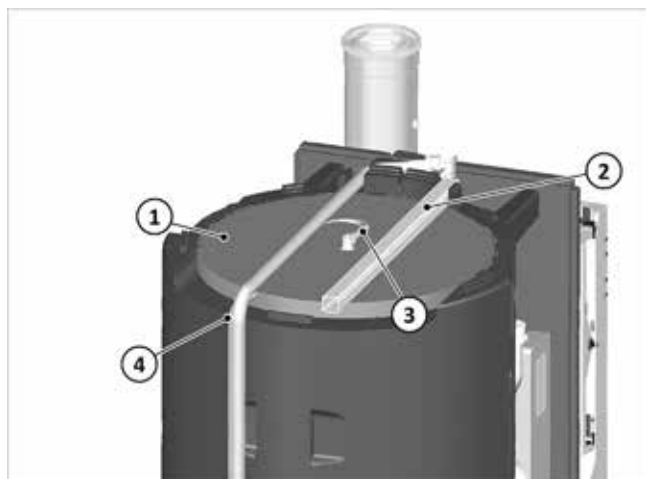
installation du rond de couvercle et des goulottes de câble
